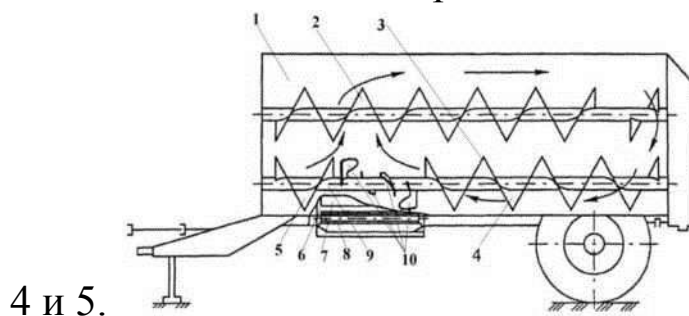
Раздатчик-смеситель кормов РСП-10 (вид сбоку): 1-бункер; 2,3-лопасти- шнеки; 4,5 - навивки витков; 6-выгрузное окно; 7 - заслонка; 8 -выгрузной транспортер; 9 - вал; 10 - лопасти-ножи.
